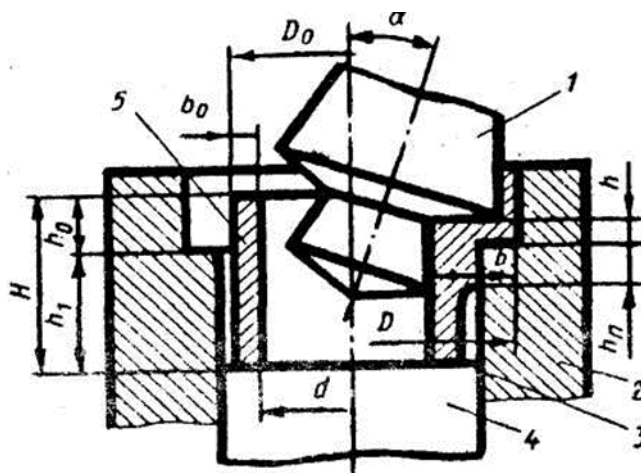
Схема формообразования наружного бурта коническим валком: 1 – валик; 2 - матрица; 3 - деталь; 4 - оправка; 5 – заготовка.
